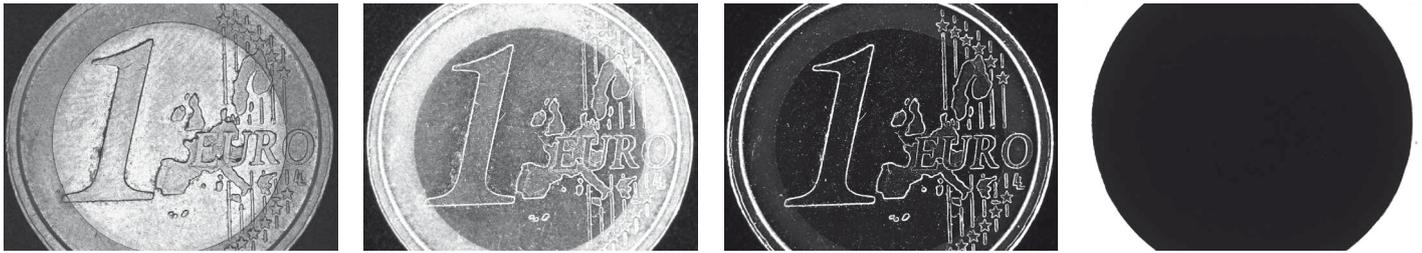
Eine Münze, beleuchtet aus verschiedenen Winkeln. Links: Hellfeld (Beleuchtungsserie FLFV), mittig links: gewinkeltes Dunkelfeld (FLDR-i100-LA3), mittig rechts: Dunkelfeld horizontal (FLDR-i100-LA1), rechts: Hintergrund (FLFL).
